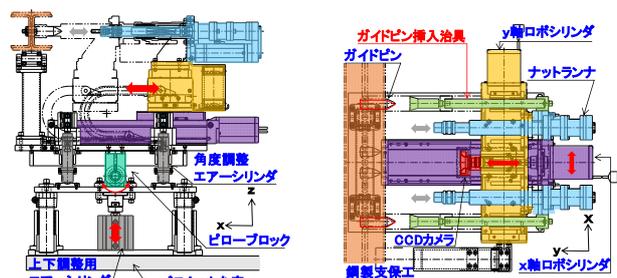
遠隔ボルト締め装置側面図(左)、平面図(右)
